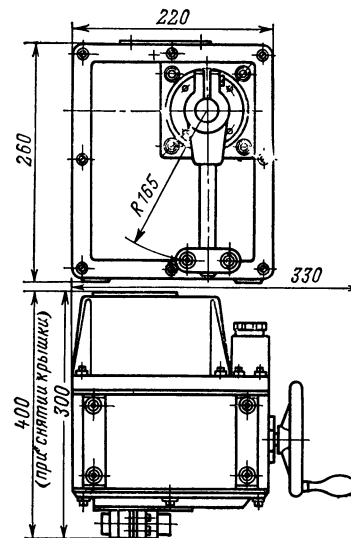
Исполнительный механизм МЭО-63/10-0,25К-73.
